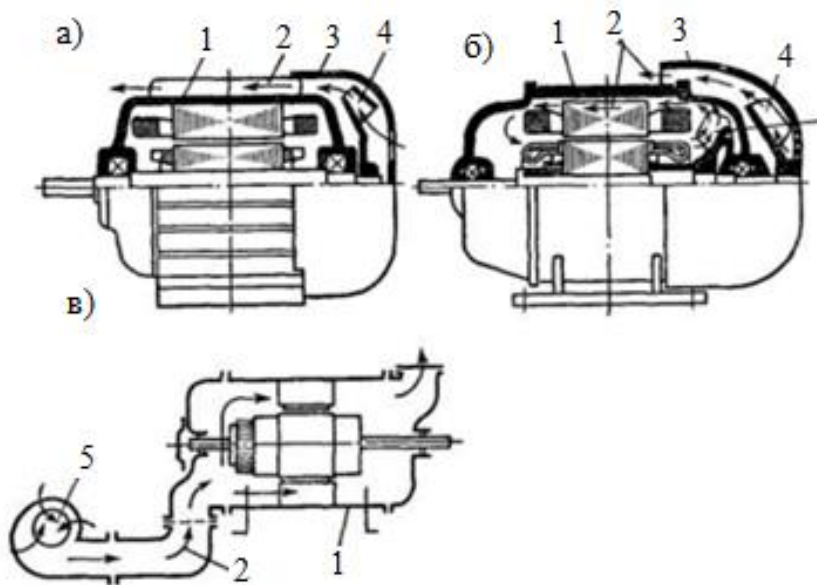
Схеми вентиляції закритих ЕМ:
